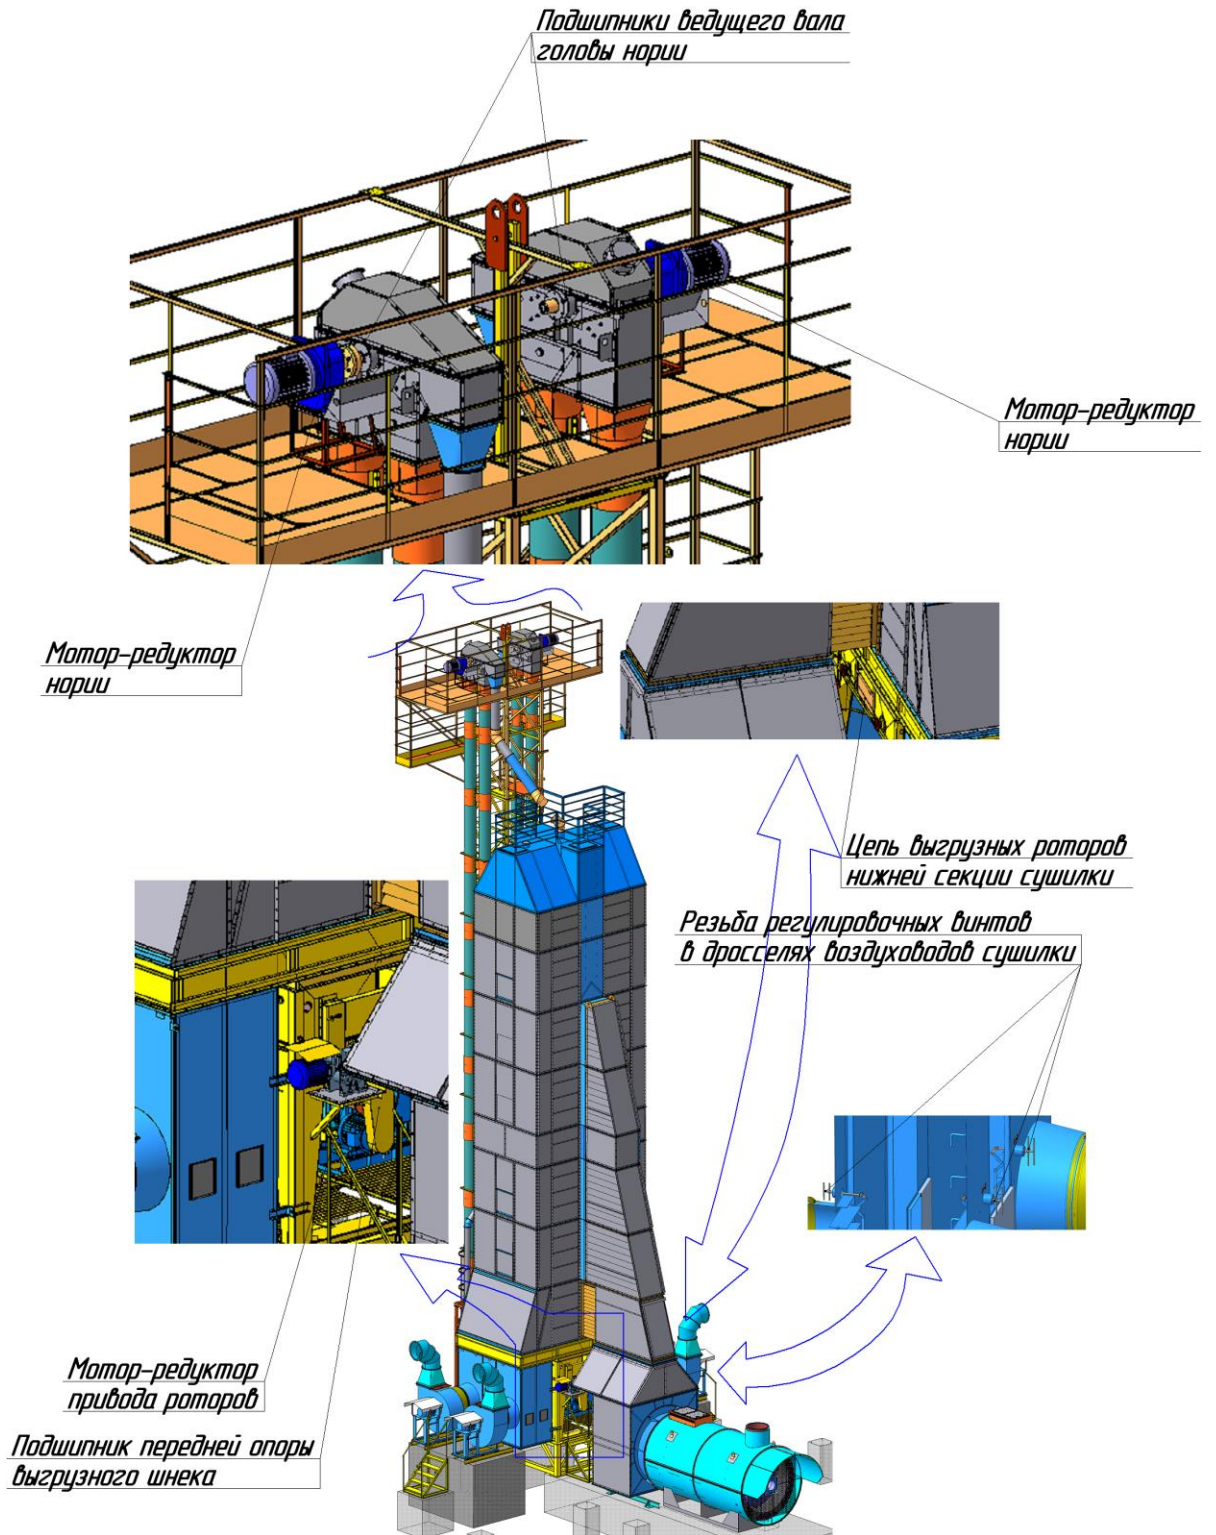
Схема смазки сушильного отделения (сушилки)
